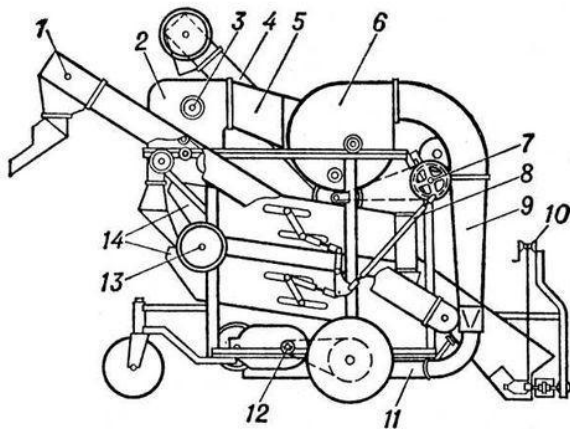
Зерноочисна машина ОВП-20А: принципова схема:
